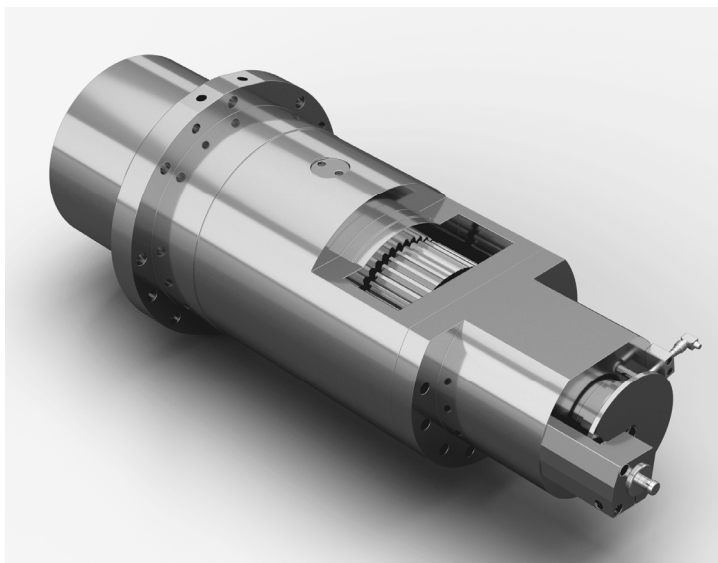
Stator a rotor vestavěného elektromotoru[7]
